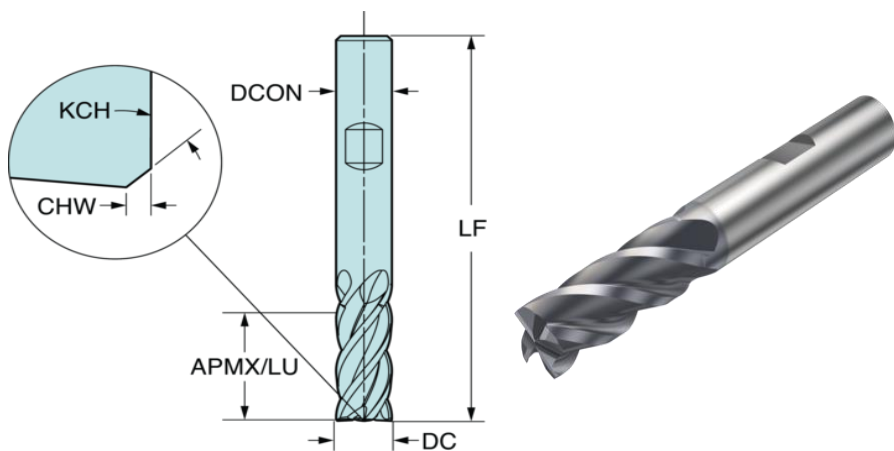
Твердосплавна фреза CoroMill® Plura 2P342-2500-PB P2BM
